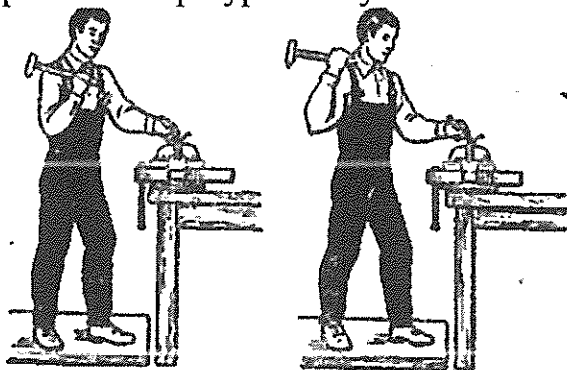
Положение корпуса и ног рабочего у тисков при рубке и приемы хватки инструмента: а - локтевой замах, б - плечевой замах
